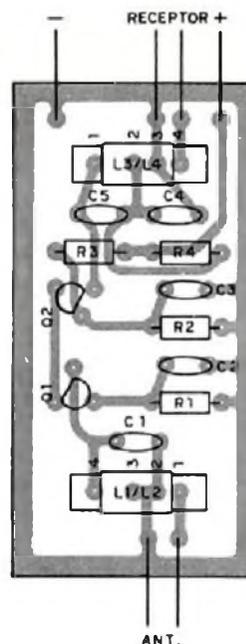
Placa de circuito impresso vista do lado dos componentes.
